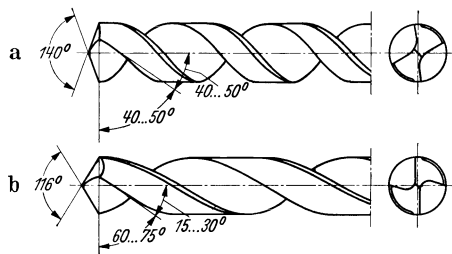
Bohrerformen für Leichtmetall-Legierungen.
